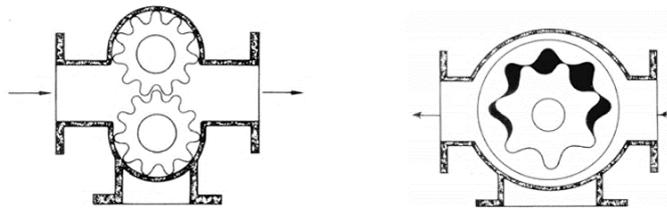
Esquema de una bomba de engranaje y bomba de lóbulos
